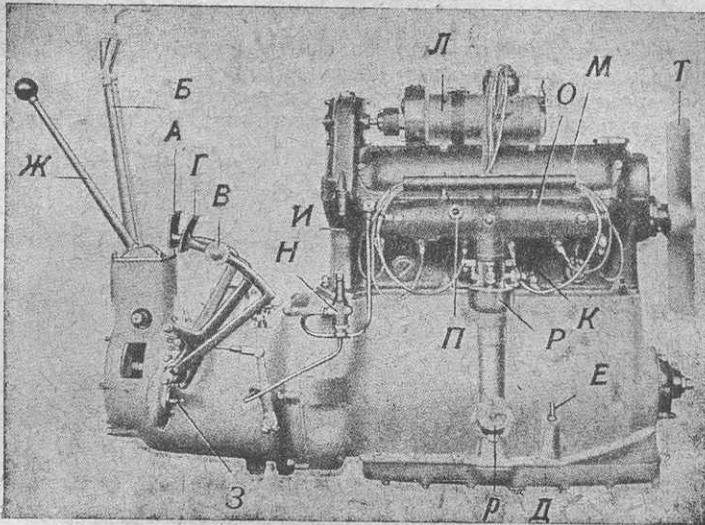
Десятицилиндровый двигатель Штейр, 15/70 л. с. (вид со стороны карбюратора).
